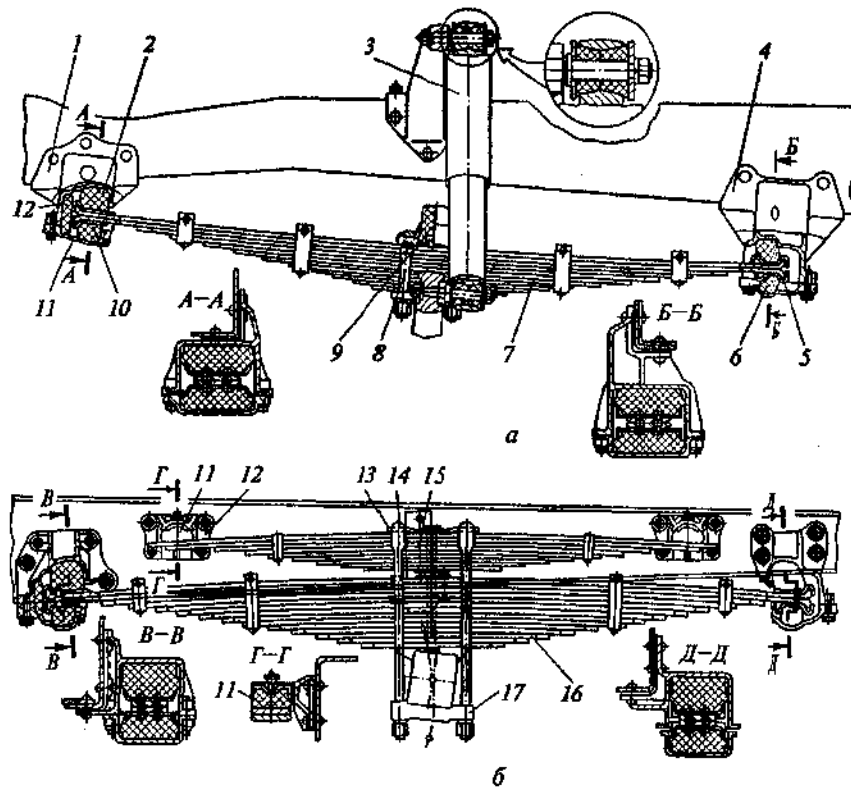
Передняя (а) и задняя (б) подвески грузового автомобиля ГАЗ: 1 и 4 — кронштейны; 2, 11 и 12 — опоры; 3 — амортизатор; 5 и 10 — чашки; 6 — крышка; 7 и 16 — рессоры; 8 и 14 — стремянки; 9 — буфер; 13 и 17 — накладки; 15 — подрессорник
